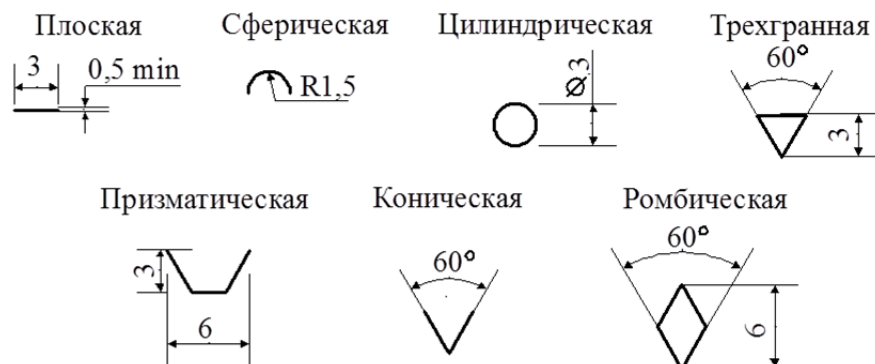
Условное обозначение форм рабочих поверхностей установочных элементов приспособлений
